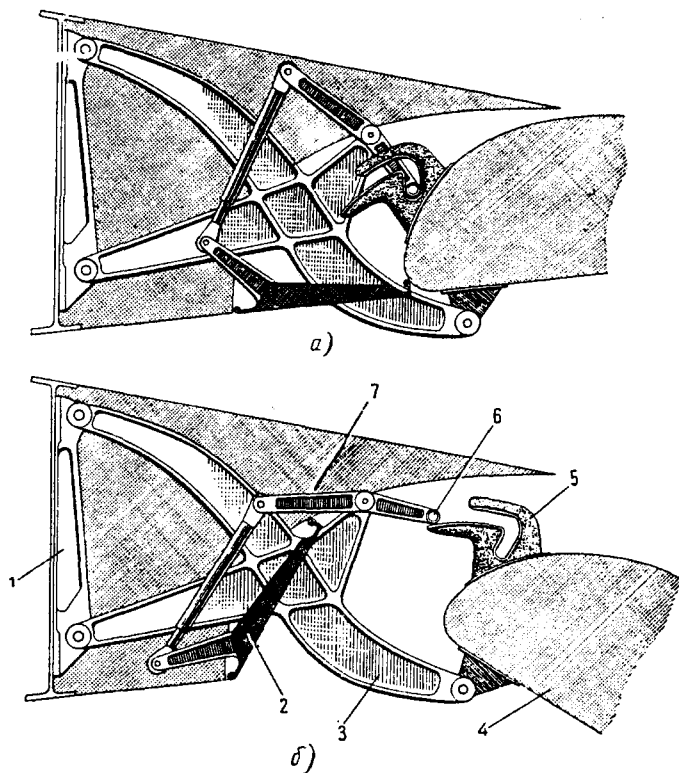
Установка подъемника однощелевого закрылка и механизм управления щитком:
